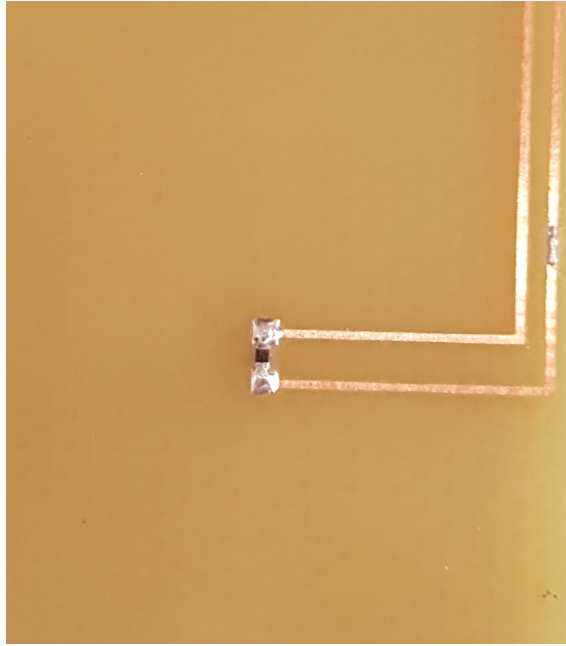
Detalle del soldado de la NTC en la cara posterior.
